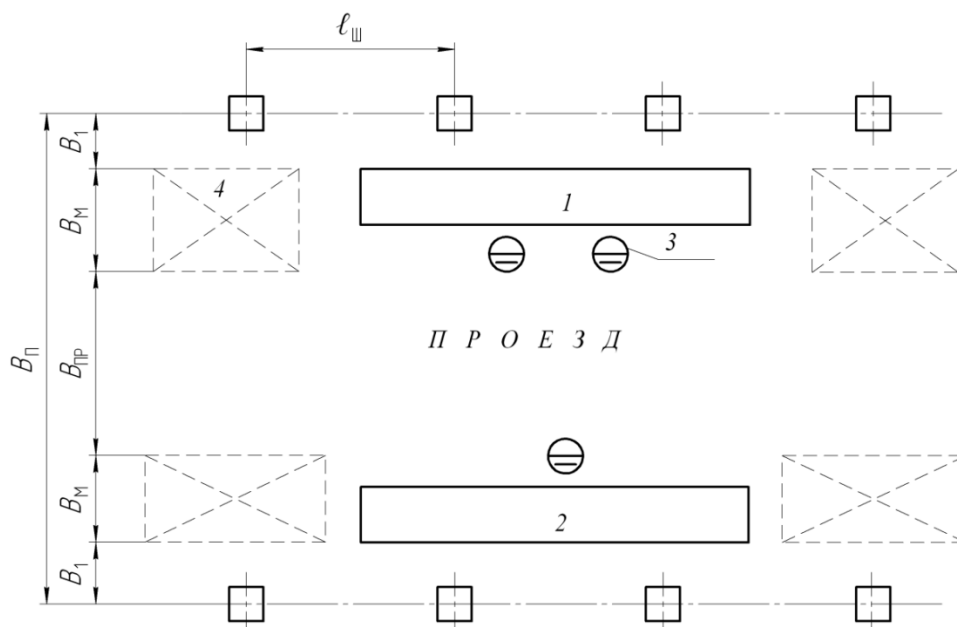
Схема планировки цеха при расположении складочных мест между рабочими местами: 1 – участок резки металла; 2 – сборочно-сварочный стенд; 3 – место обслуживающего персонала; 4 – складочное место
